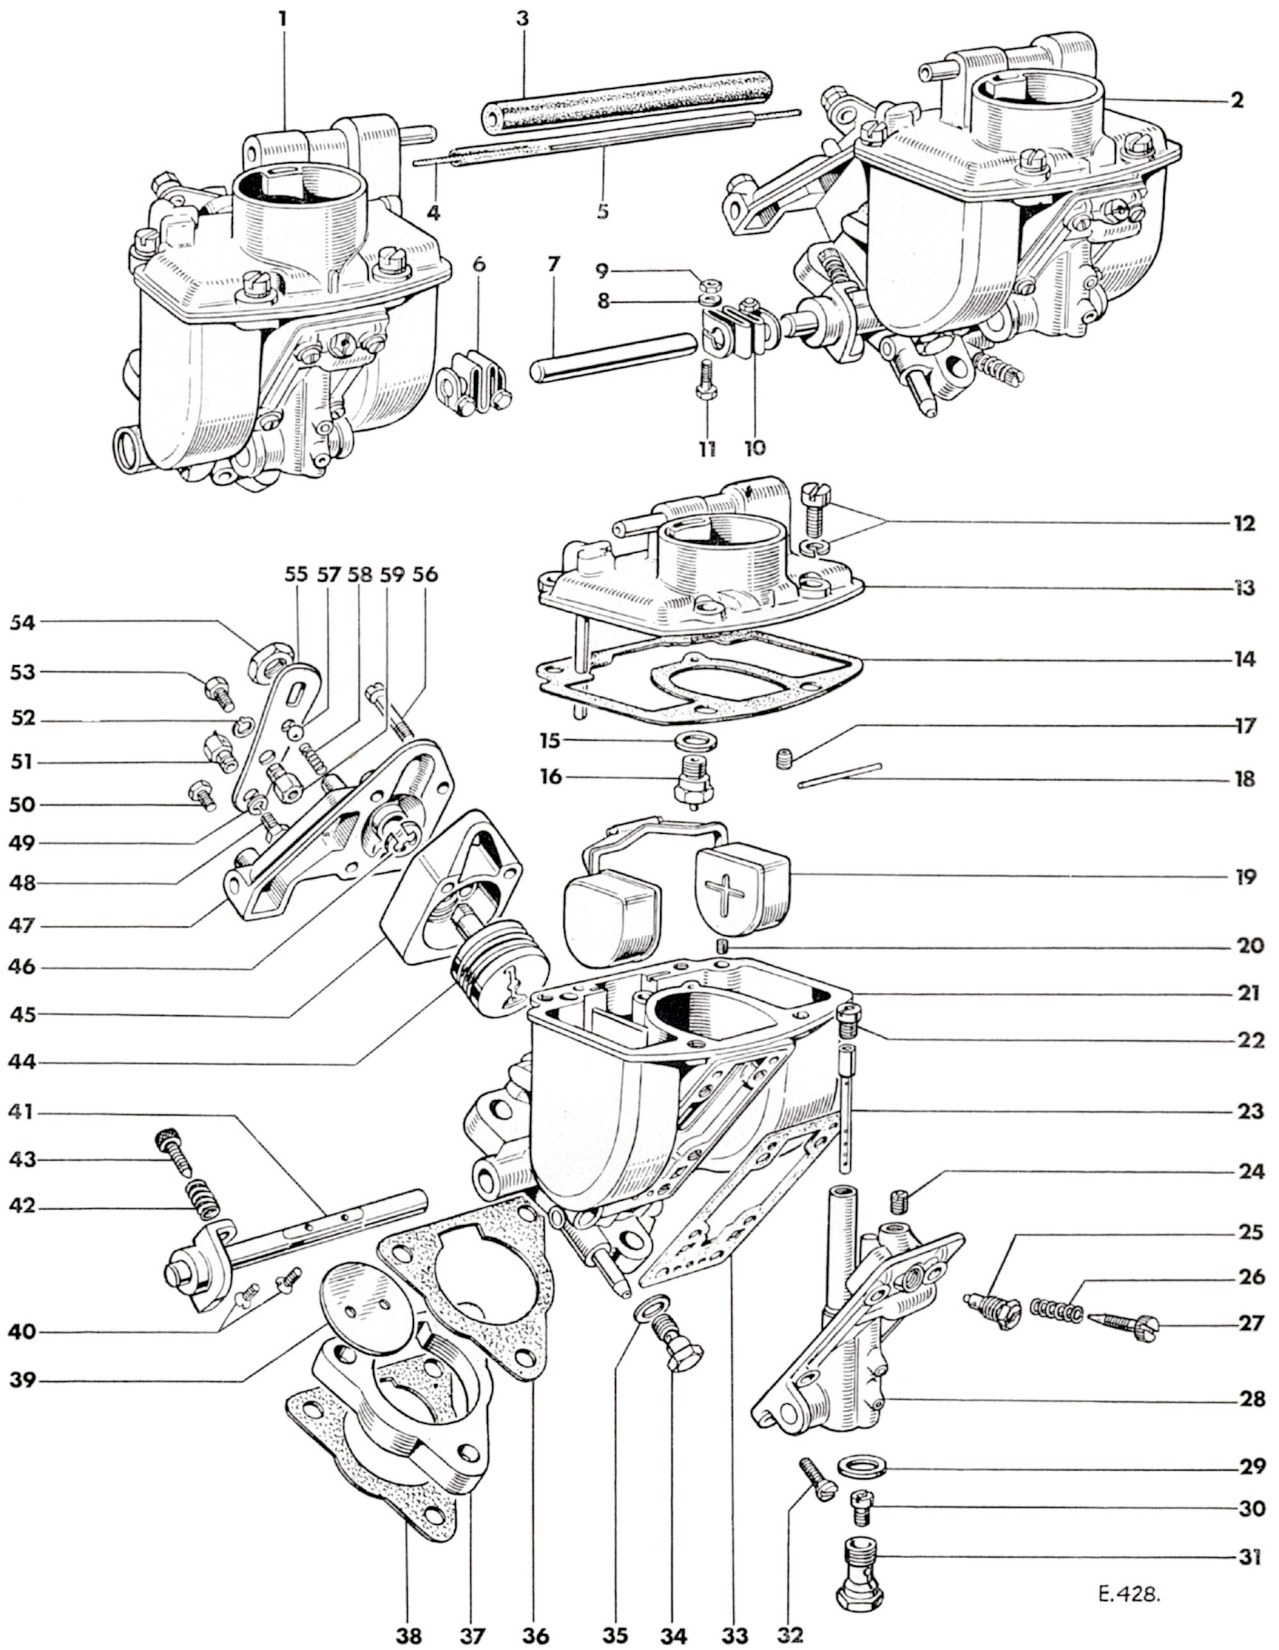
Vue éclatée du carburateur semi-inversé Solex B32.1H
